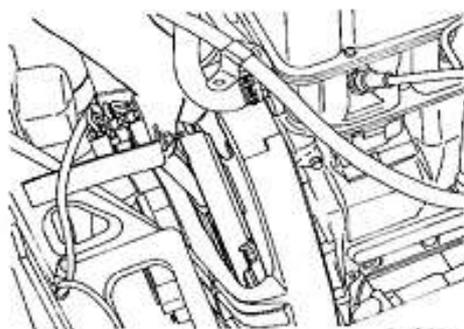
Dépose de l'ensemble couvercle d'embrayage
